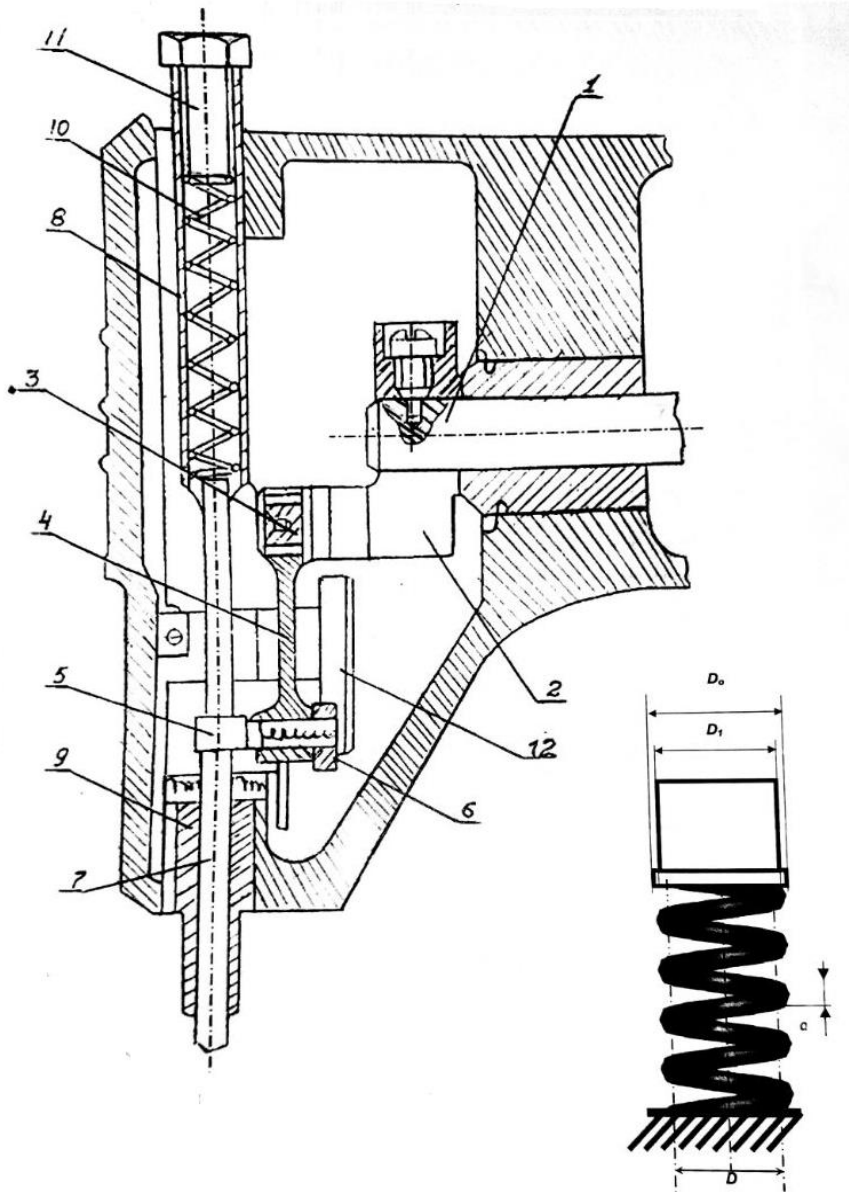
Конструктивная схема механизма иглы с упругими элементами 1-вал, 2-кривошип, 3-палец, 4-шатун, 5-поводка, 6 – ползун, 7-игловодитель, 8,9-втулка, 10-пружина, 11-винт, 12-паз.
